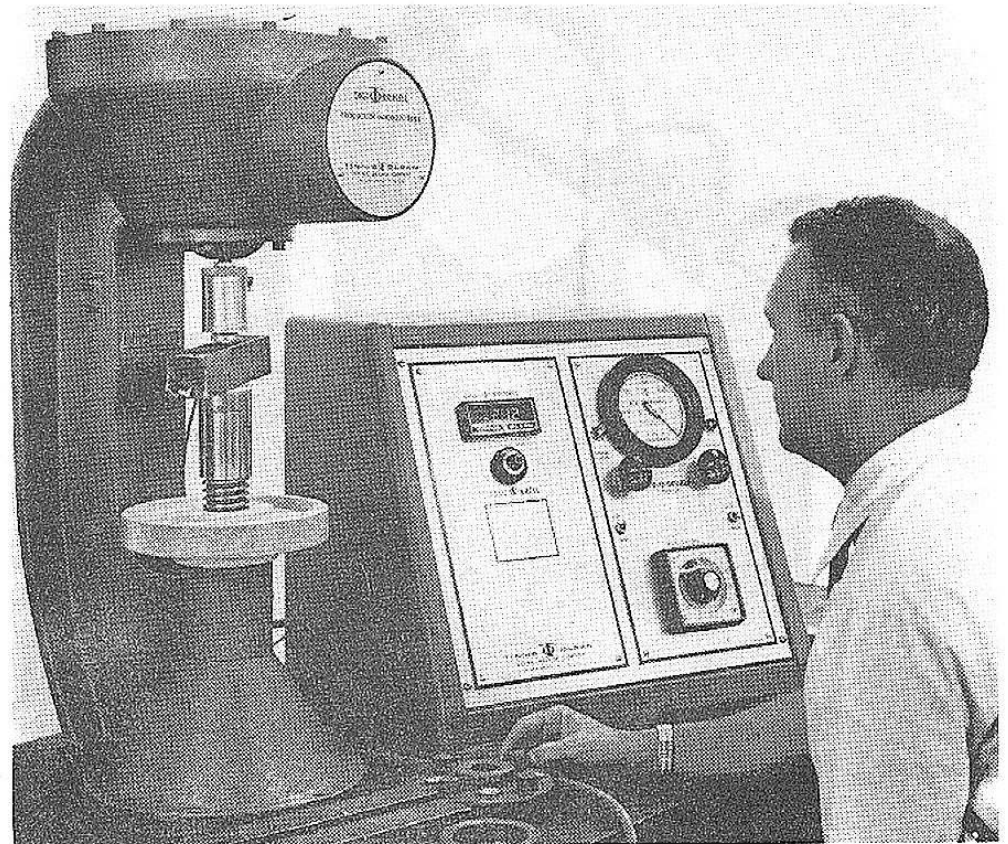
Una máquina de ensayo de dureza. (Foto cortesía de Tinius Olsen Testing Machines Co., Inc.)
